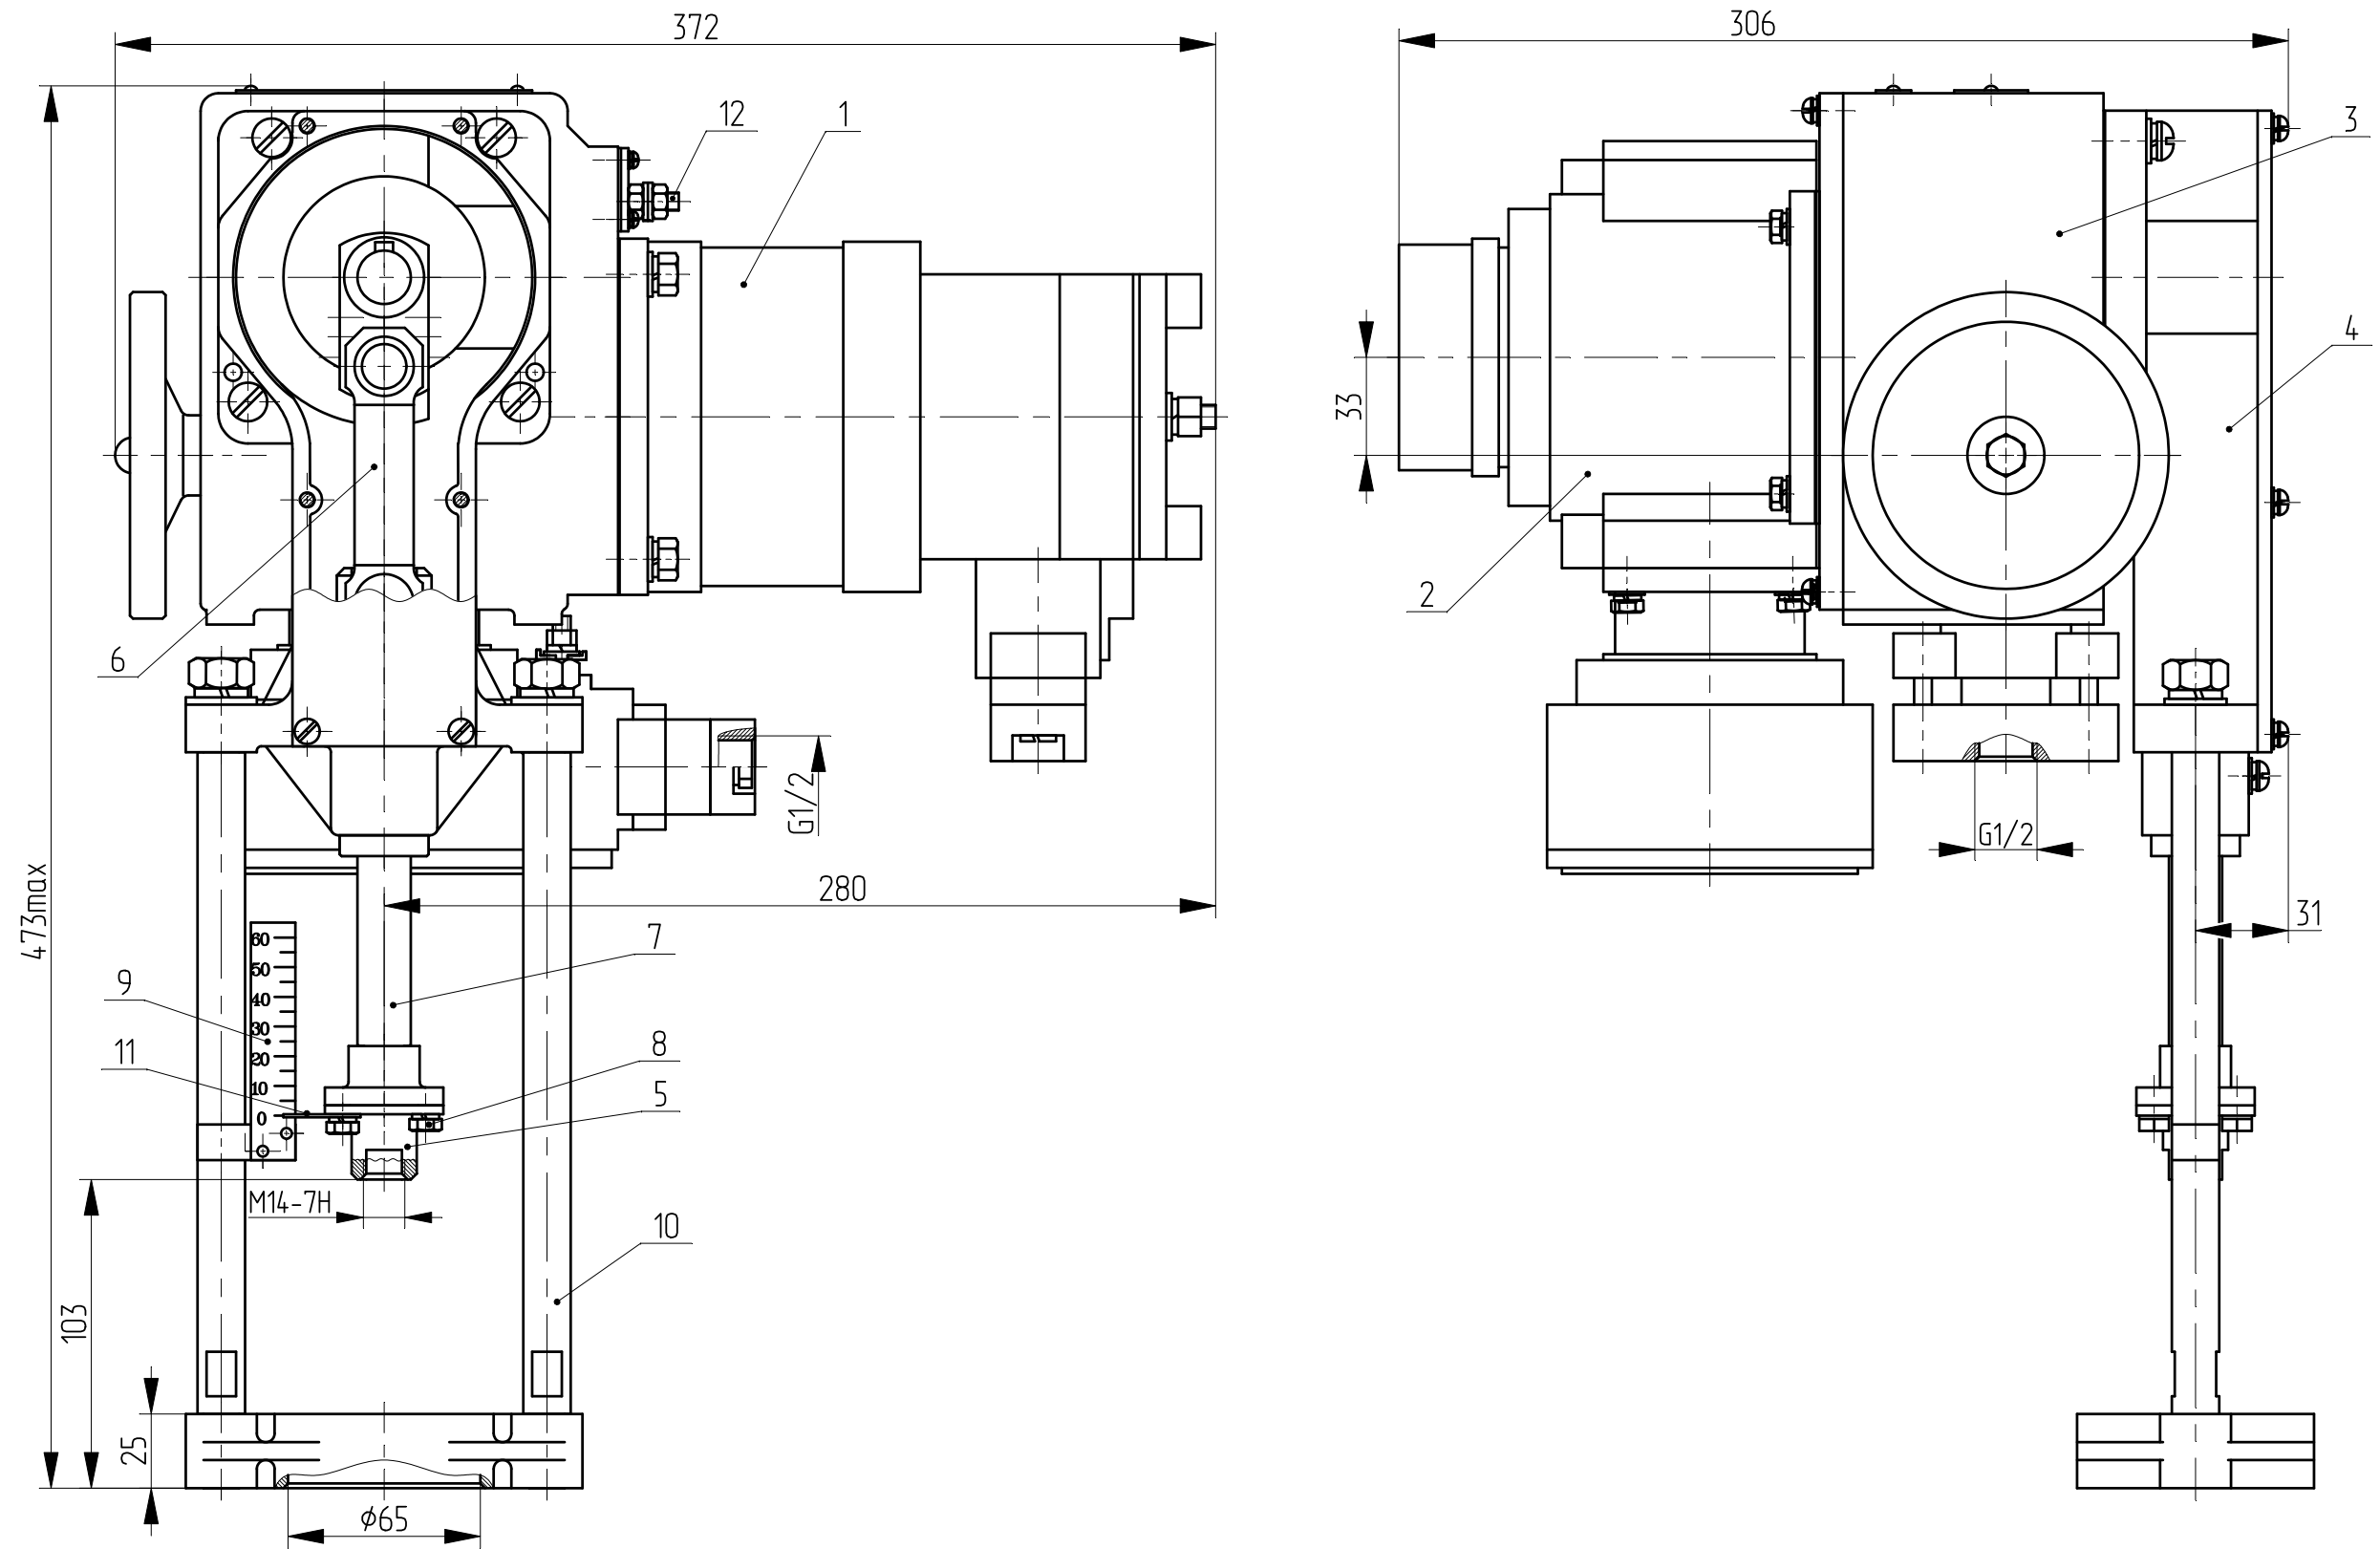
Общий вид, габаритные и присоединительные размеры МЭПК-6300-ИВТ4-01
